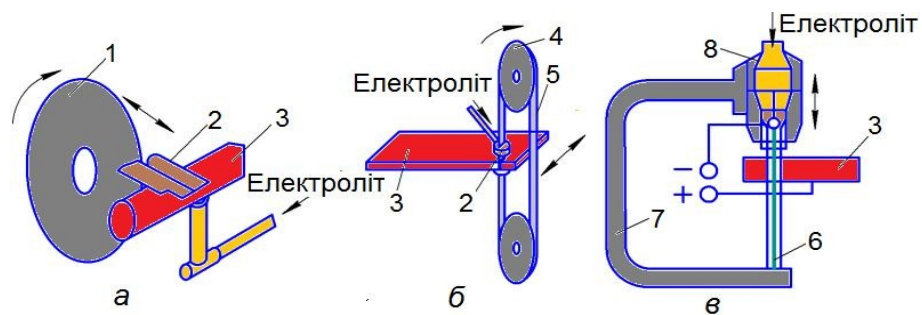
Схеми установки для розмірної електрохіміко-гідралічної обробки шляхом різання: а – диском; б – стрічкою; в – провідом: 1 – диск; 2 – напрямна; 3 – деталь; 4 – барабан; 5 – стрічка; 6 – провід; 7 – скоба; 8 – головка
